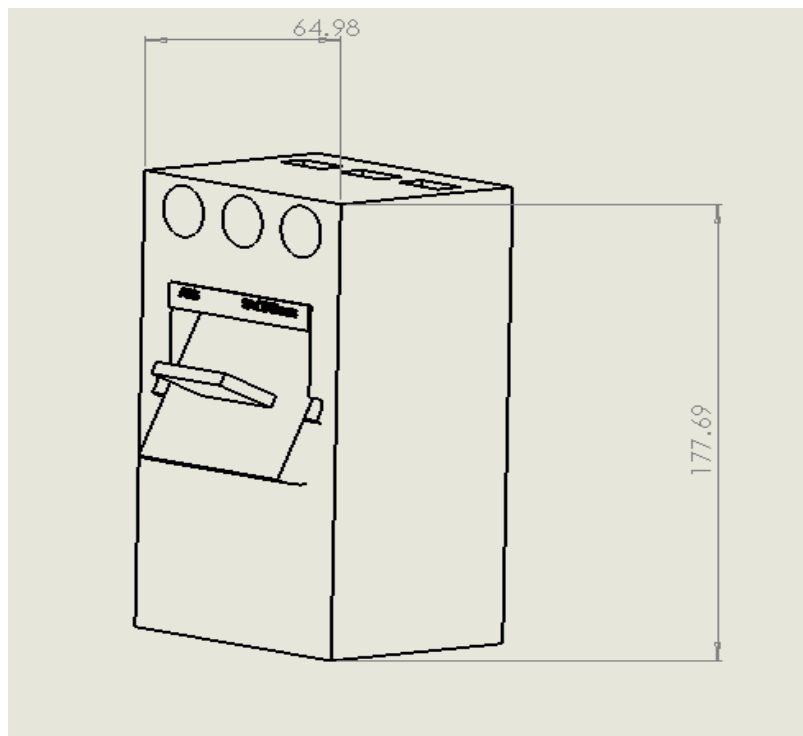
contactor de motor de maquina compactadora con bobinas a 24 V DC, realizado en SolidWorks
